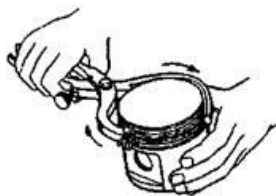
Очистка нагара в канавках поршней с помощью приспособления
